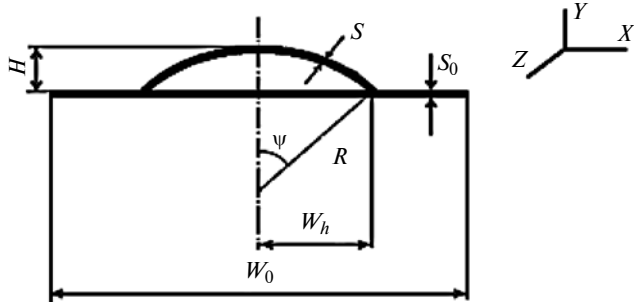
Расчетная схема деформирования прямоугольного сварного листового пакета
